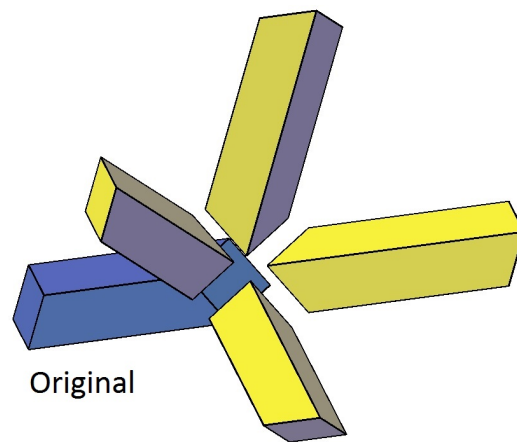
Explosionszeichnung und Lage der vier Positionen des Prismenstücks am zusammengebauten Modell
